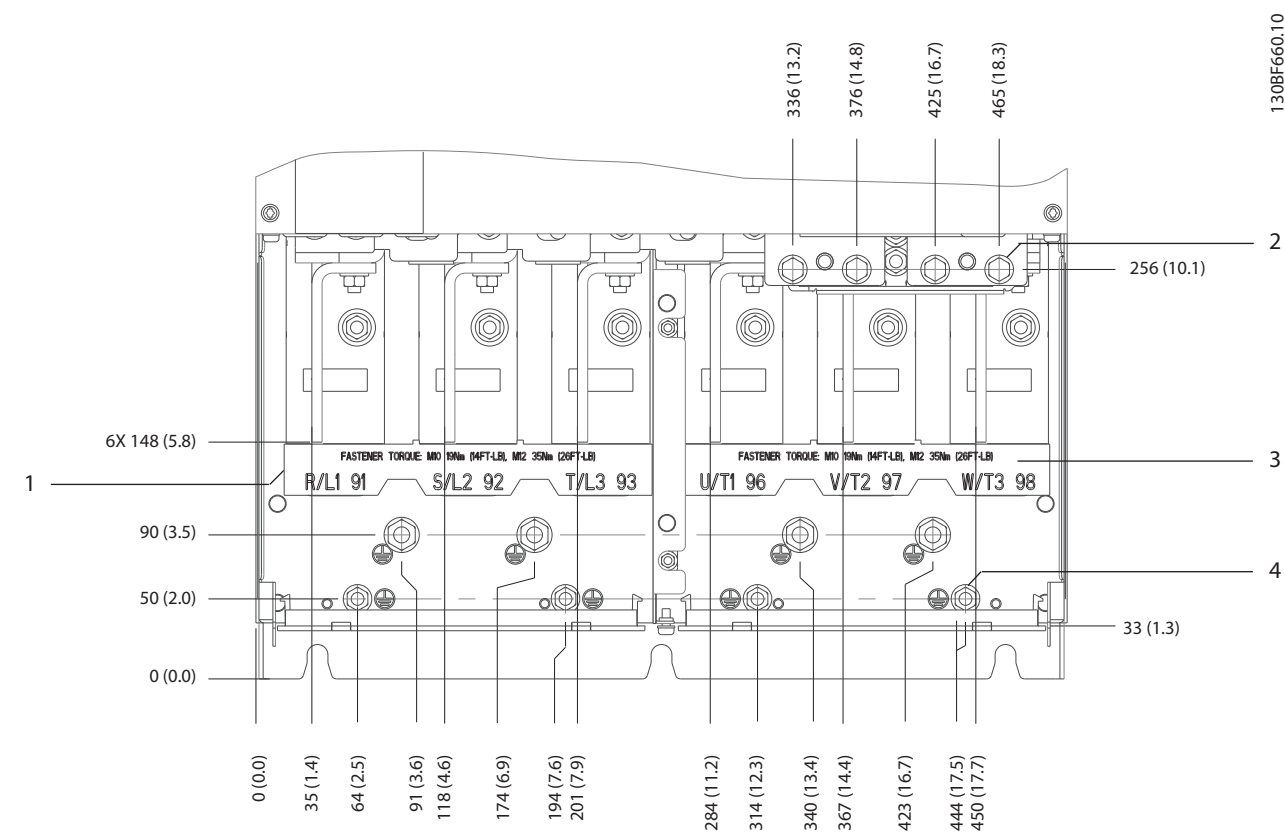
Dimensões do Terminal E2h (vista frontal)
